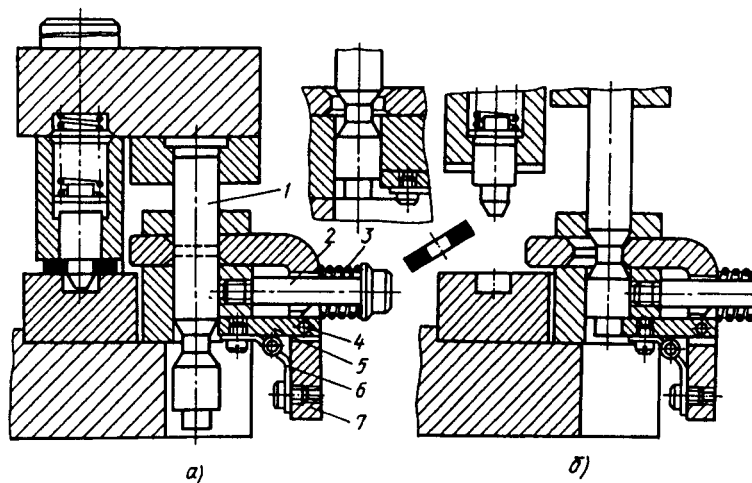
Шиберный механизм для подачи заготовок в вытяжной штамп
